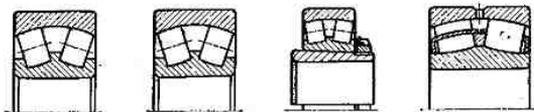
Роликоподшипники радиальные сферические двухрядные типов: а — 3000; б — 113000; в — 12600; г — 53000
